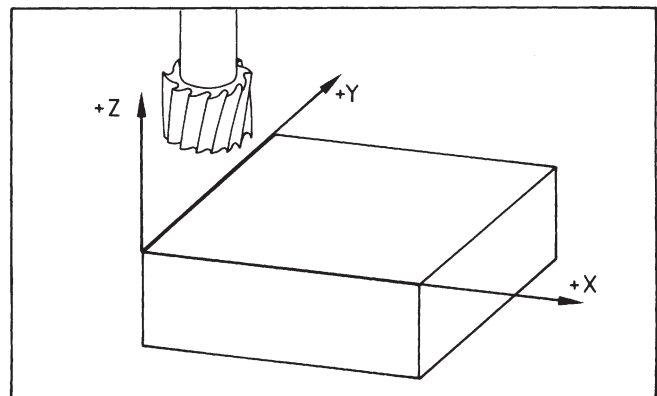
Fräsbearbeitung mit einer Senkrecht-Werkzeugfräsmaschine
